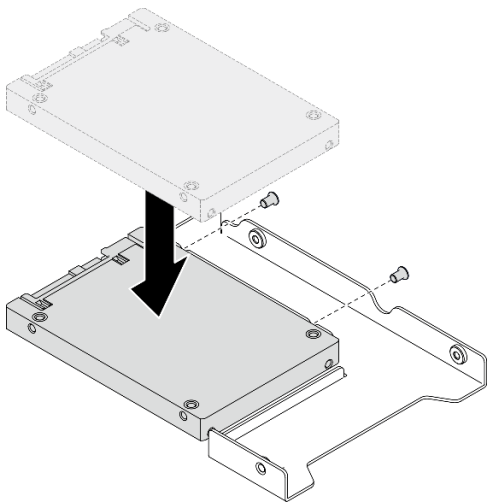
Установка 2,5-дюймового диска в адаптер для дисков
